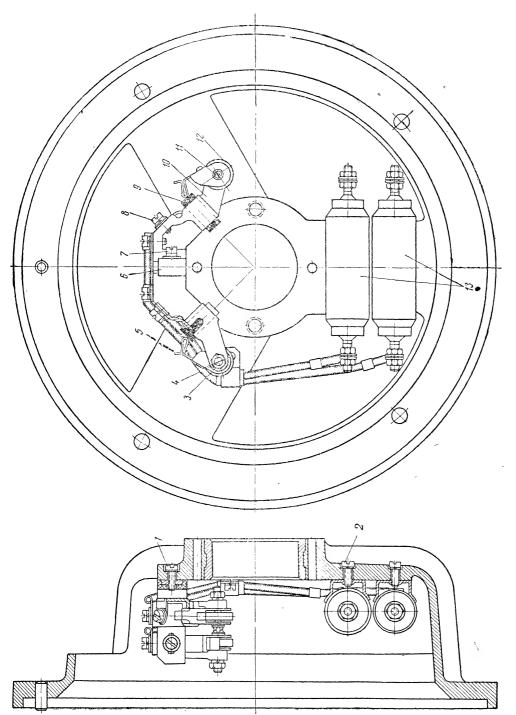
Подшипниковый щит со стороны контактных колец: I—винты, крепящие палец к щиту; 2—винты, крепящие блок конденсаторов к щиту; β —гайки оси нажимной пружины; 4—ось нажимной пружины; 5— нажимной палец; 6—палец щеткодержателей; 7—винты, крепящие щеткодержатели к пальцу; 8—винты, крепящие щетку; 9— цетка; 10— шеткодержатель; 11— пружиное кольцо; 12— нажимная пружина; 13—блок проходных конденсаторов
